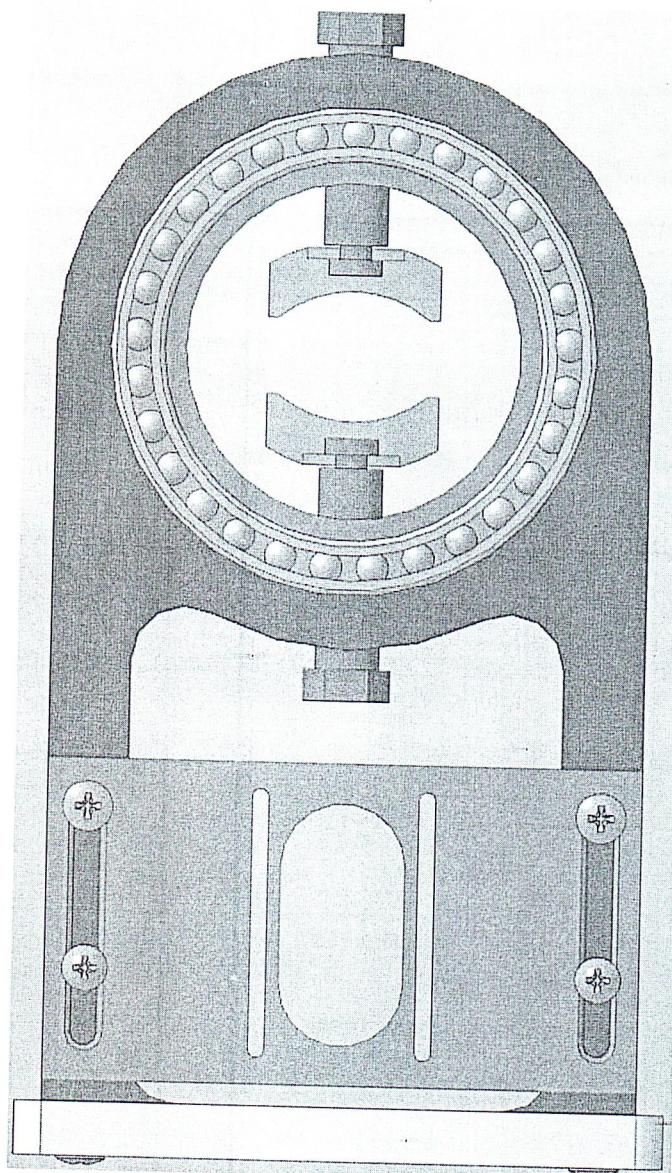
3D сборка сварочного вращателя «закрытого»
